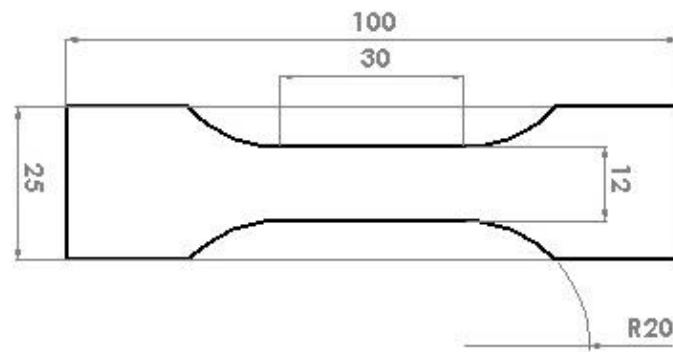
Geometria e dimensões de um provete de ensaio de tração
